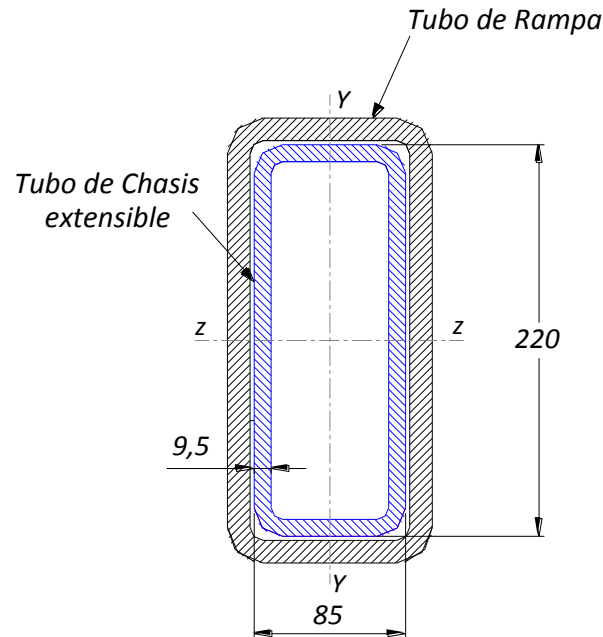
Dimensiones de la viga del chasis extensible.
